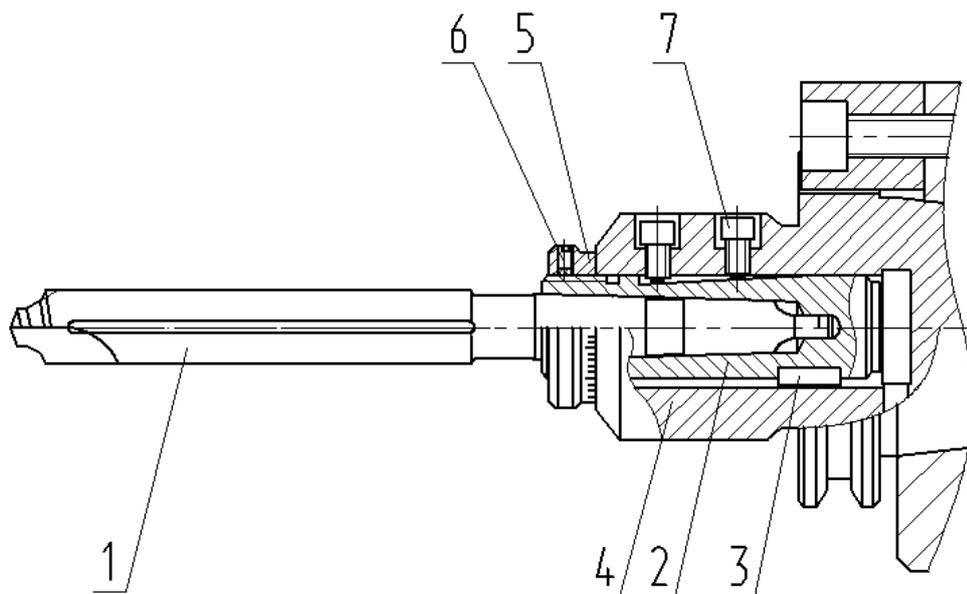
Фрагмент шпиндельного узла сверлильного станка.
